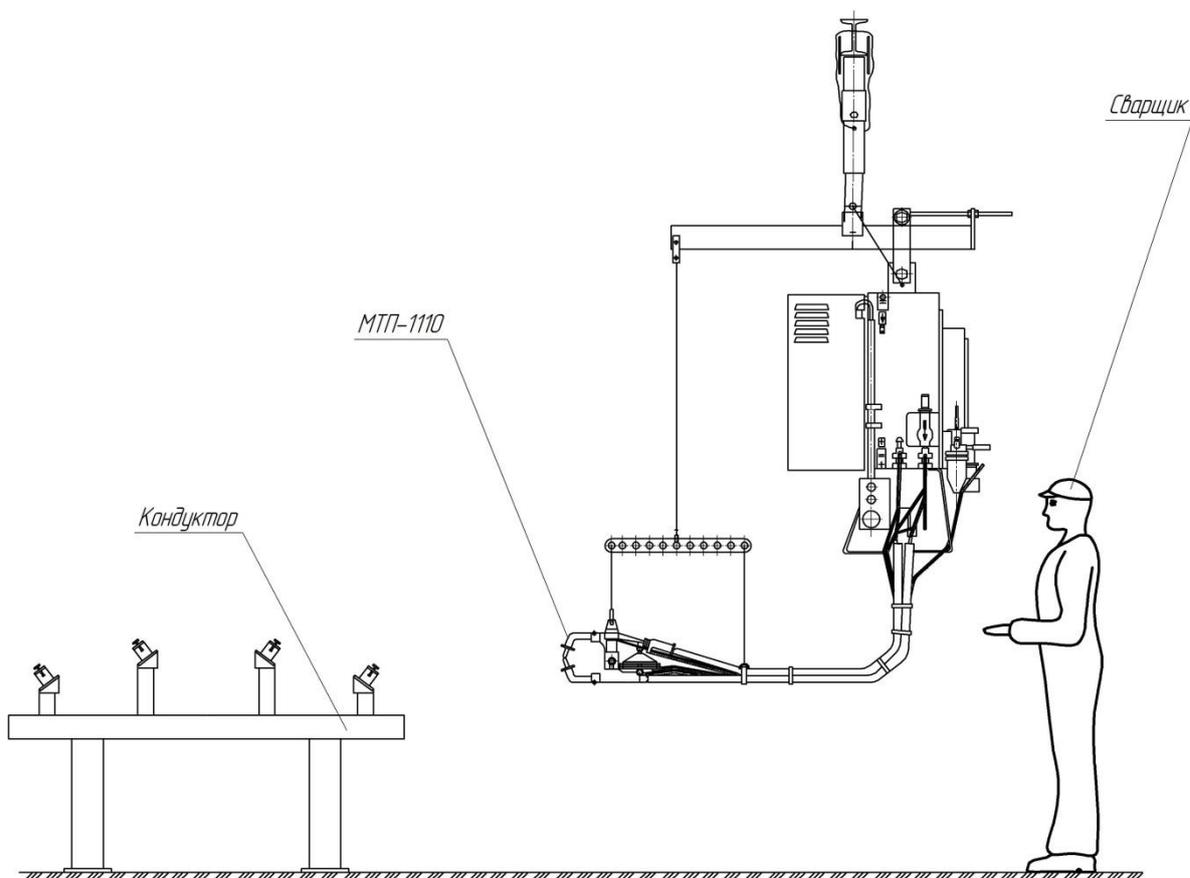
Базовая технология сборки-сварки узла
